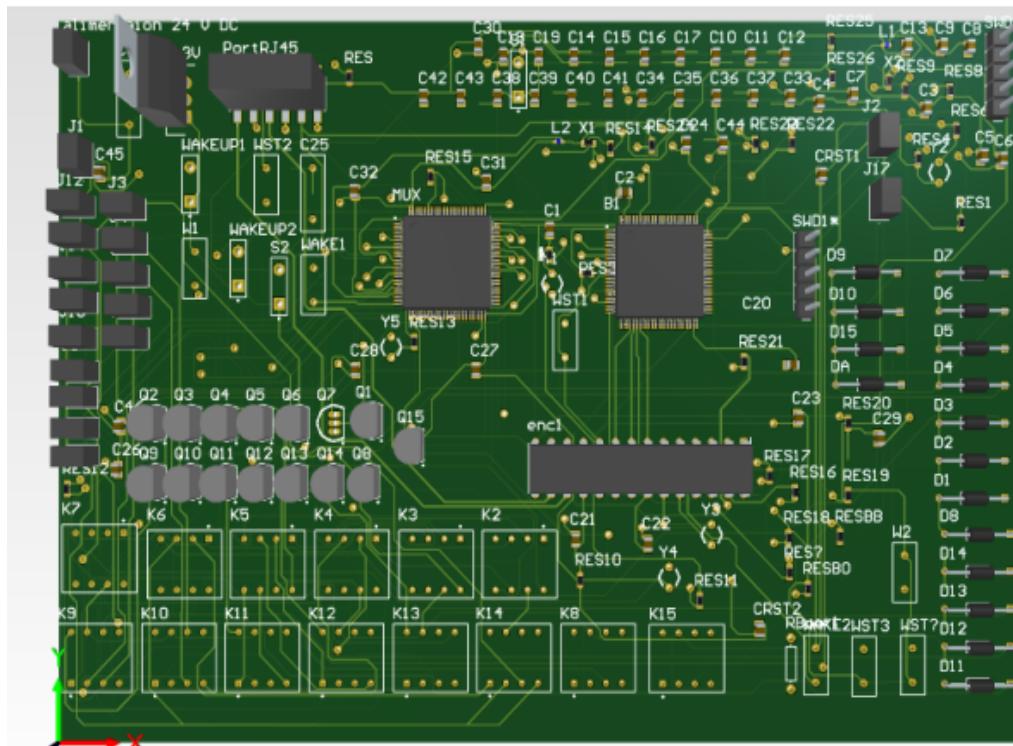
Vue 3D de la PCB : Top Layer
